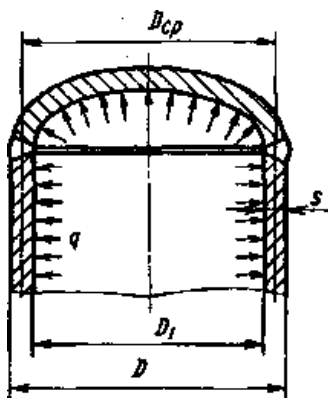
Сварное соединение дна сосуда с обечайкой (корпусом).
